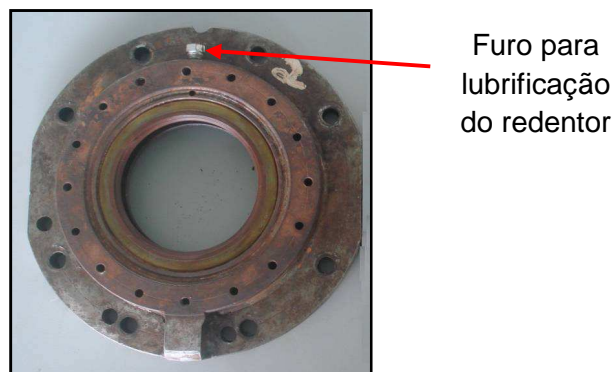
Furo para lubrificação externa do retentor, usinado na parte superior da tampa.
